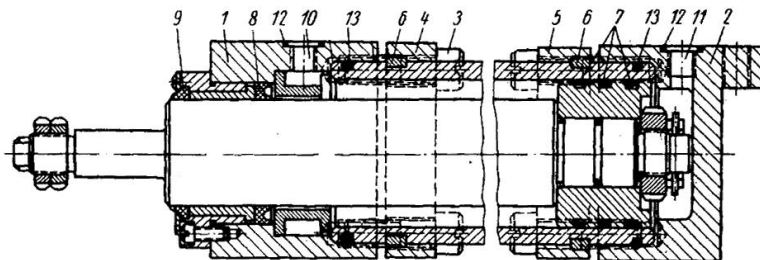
Конструкция гидроцилиндра стыкового монтажа
